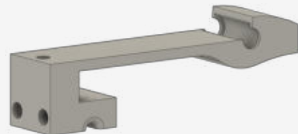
3D-gedrucktes Rumpfmittelstück
